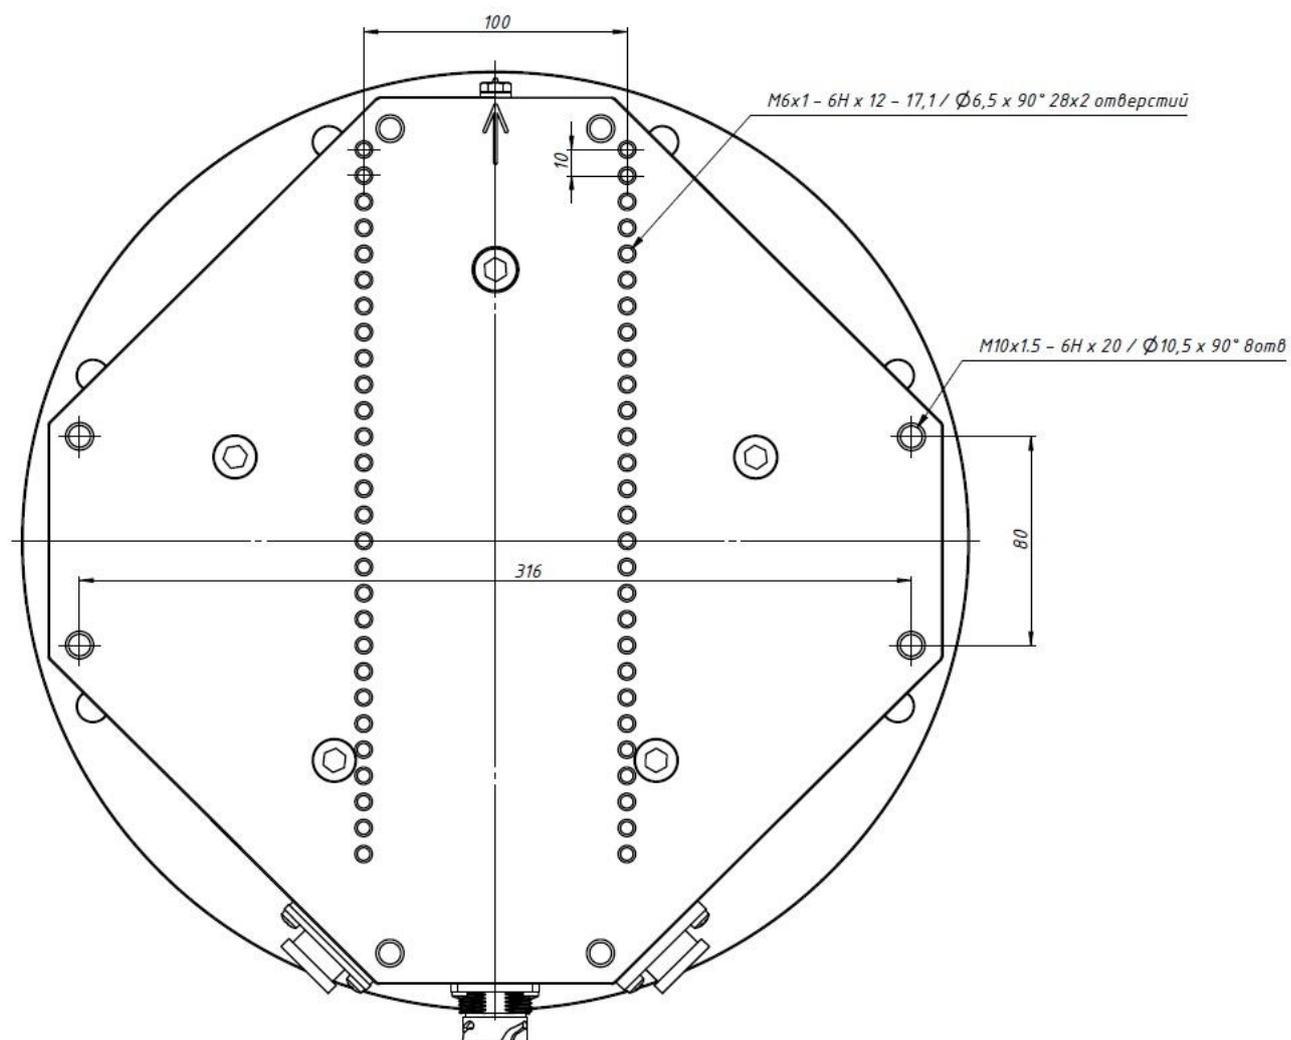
Присоединительные размеры поворотной платформы (для полезной нагрузки)
